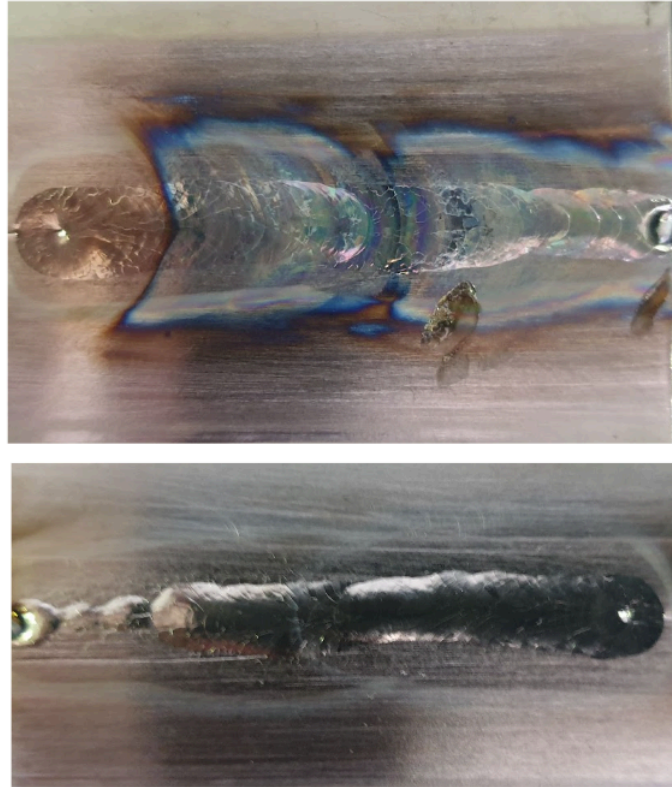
Echantillon 01 (soudure avec un courant continu)
